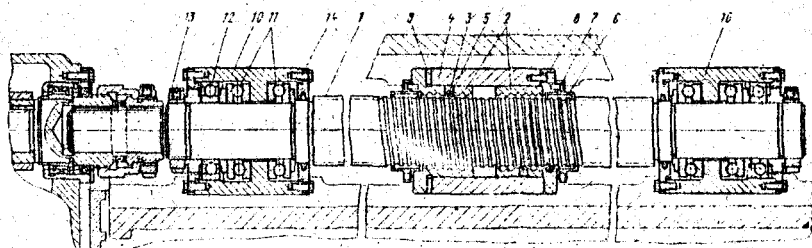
Конструкция шариковой передачи винт-гайка качения
